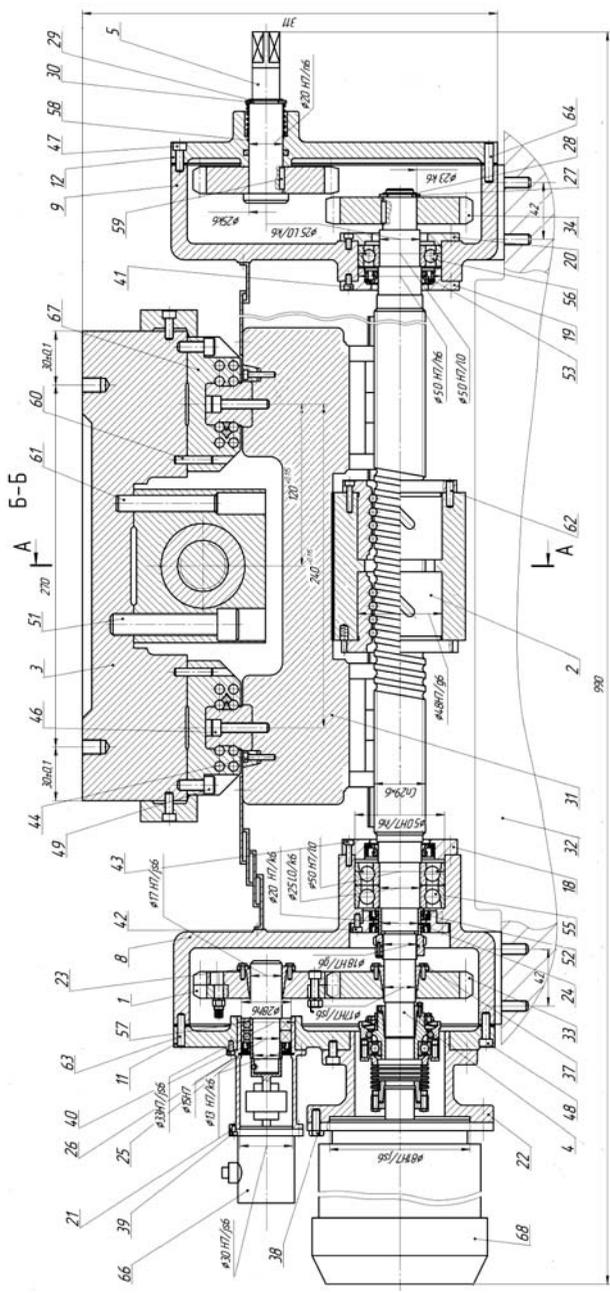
Крестовый суппорт с горизонтальным приводом продольной подачи салазок токарного станка с ЧПУ :
